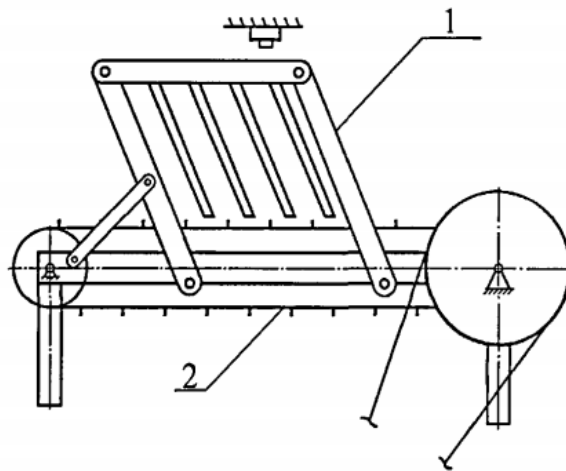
Схема подрібнювача соковитих кормів і баштанних транспортерно-ножового типу
